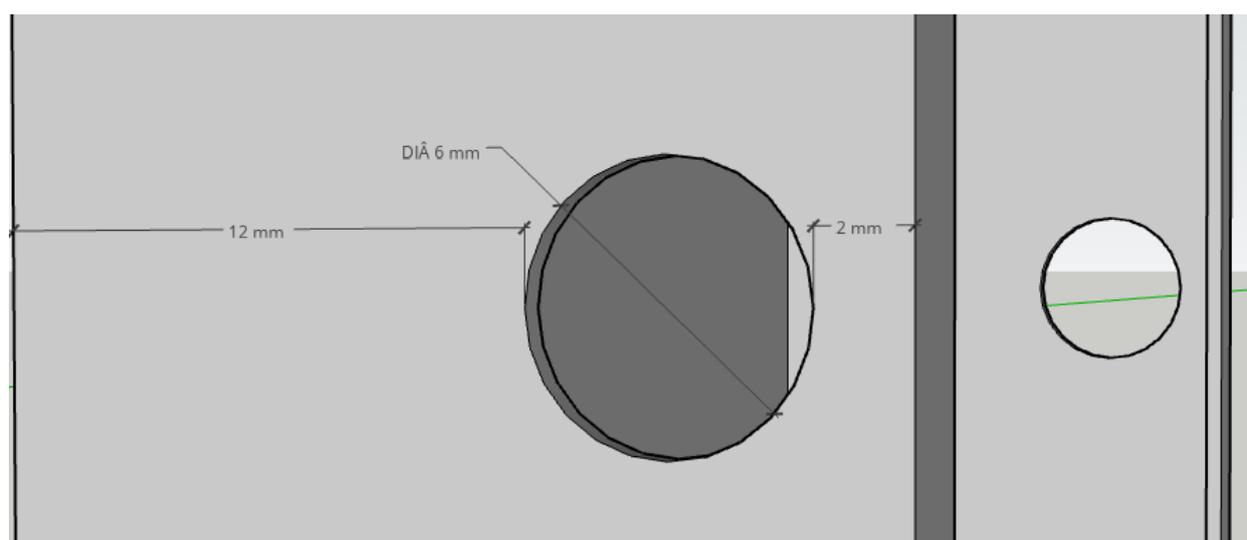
Corte da seção transversal do perfil de enrijecimento com dimensões e posicionamento dos furos
